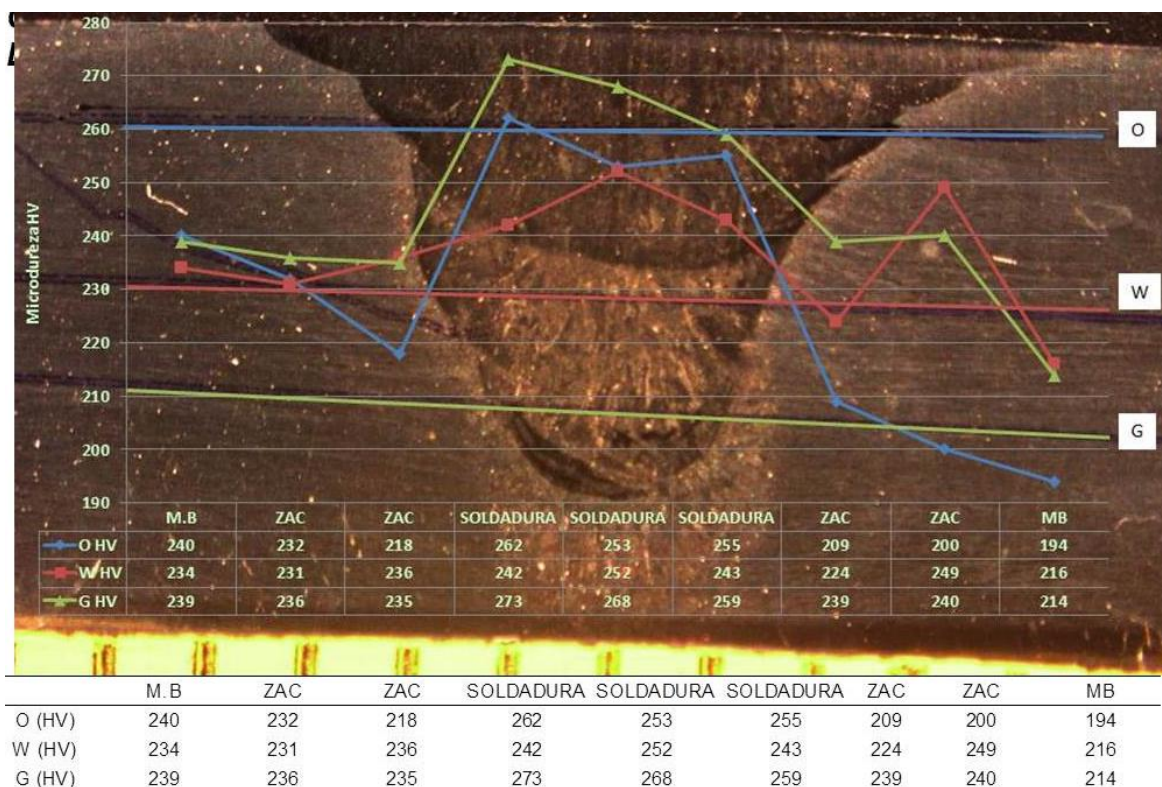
10 Perfil de dureza practicado a la unión soldada de DSS 2205 mediante GTAW
